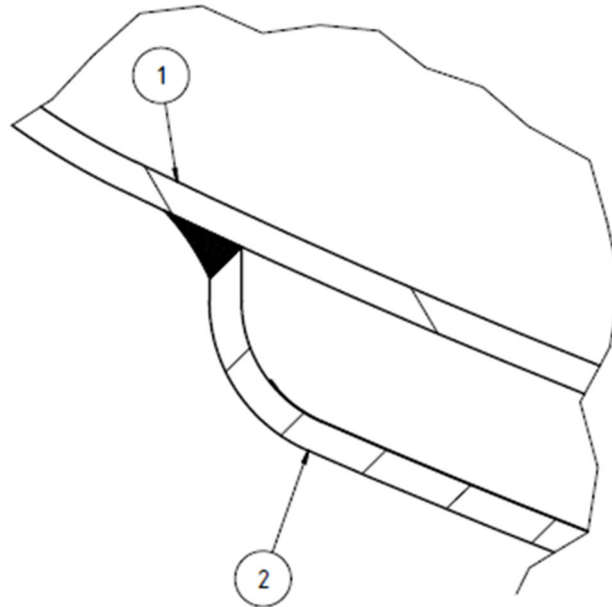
Schweißdetail Behälterboden und gewölbter Scheibe<sup>23</sup>
